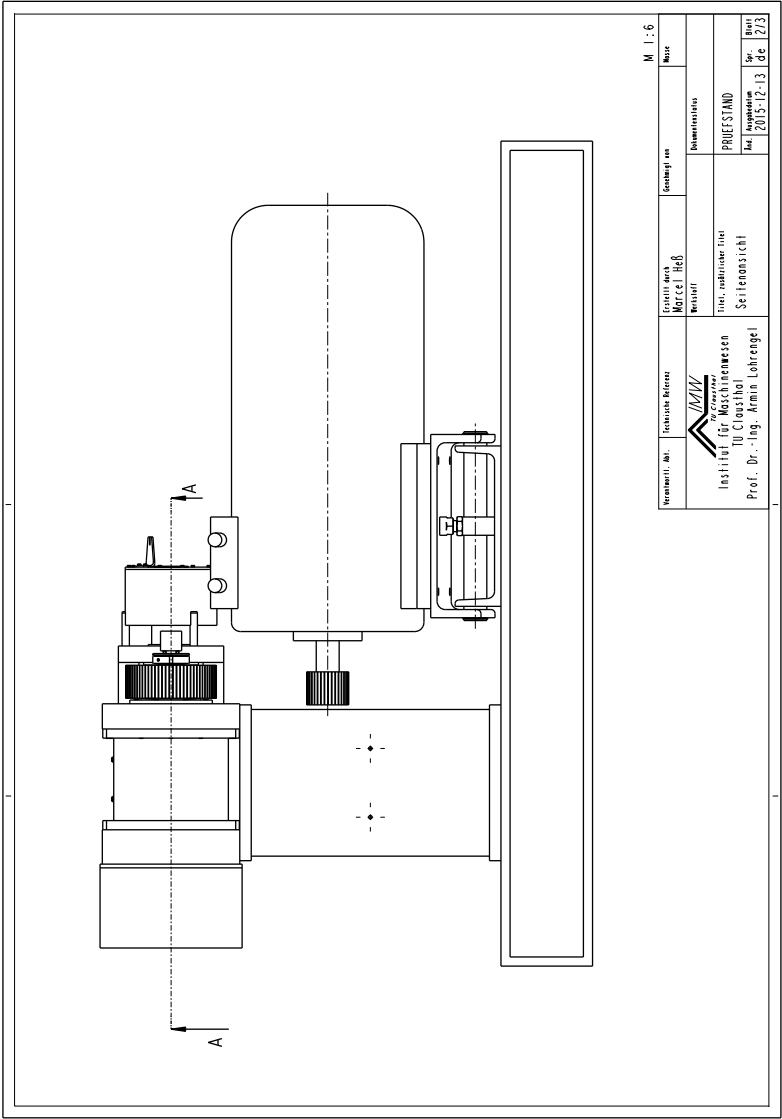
Seitenansicht des Druckkammprüfstandes: keine Abbildung der Zahnriemen.
